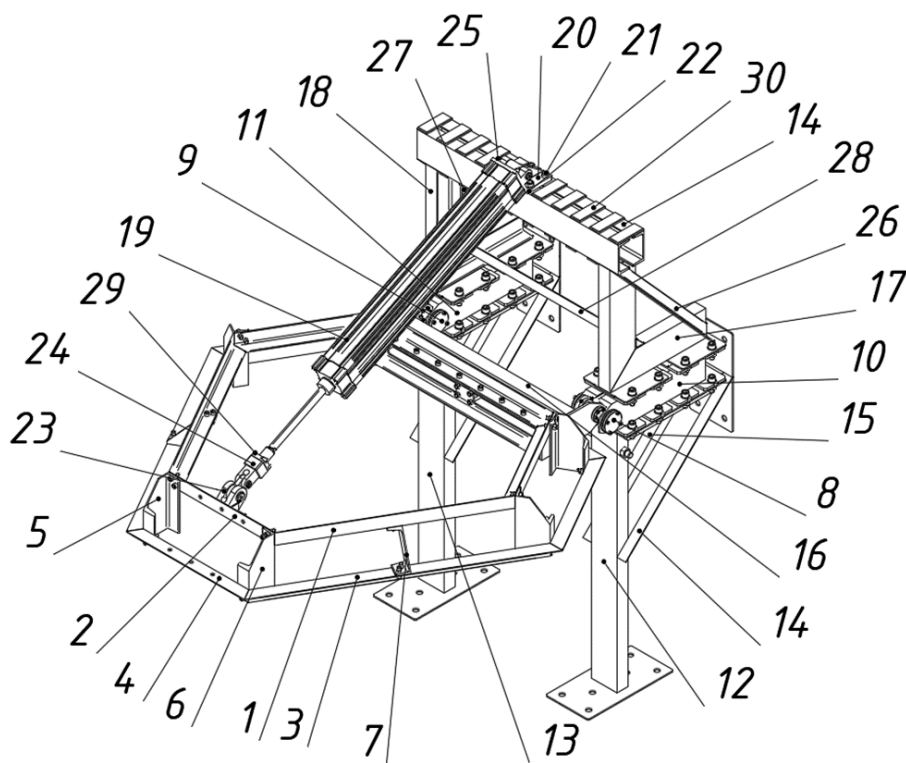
Конструкція поворотної рами роботомеханічного комплексу.
